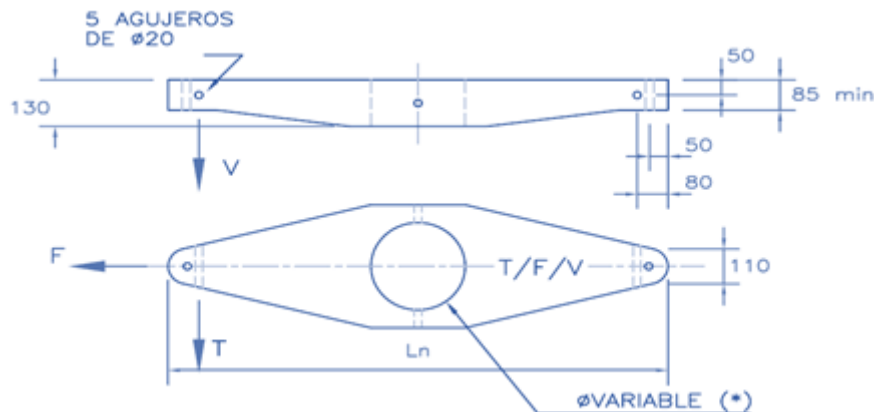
Geometría y dimensionamiento en mm de la cruceta simétrica
